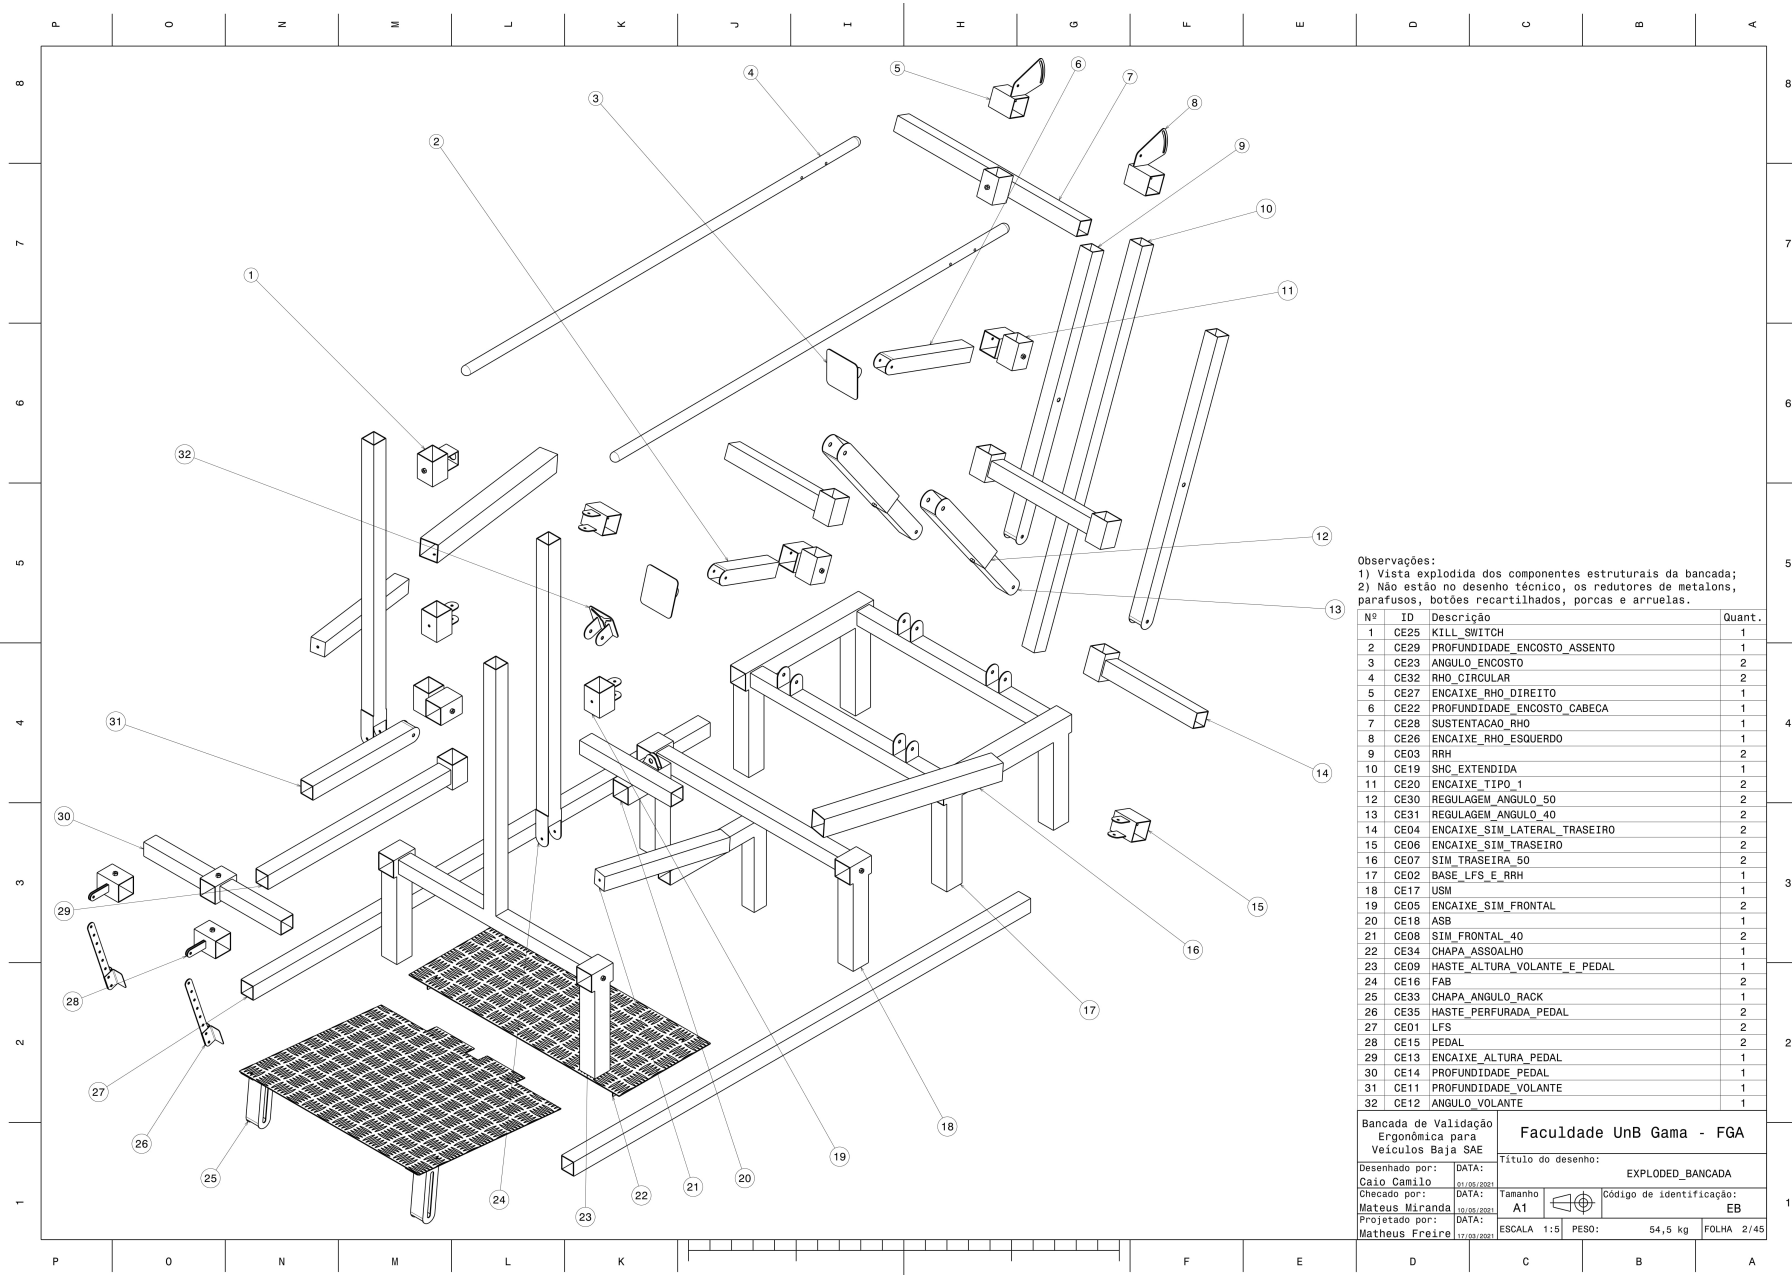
Desenho técnico do conjunto explodido. Fonte: Autores (2021).
